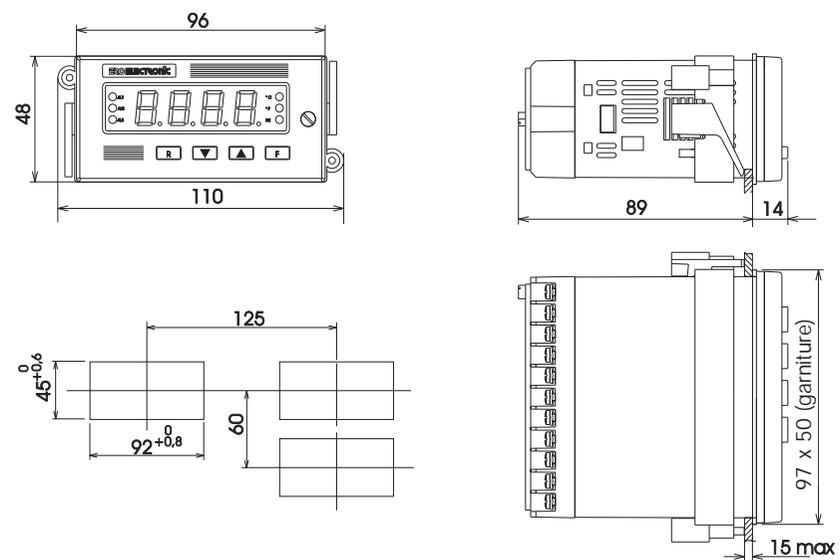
A TIS - DIMENSIONS ET PERCAGE
